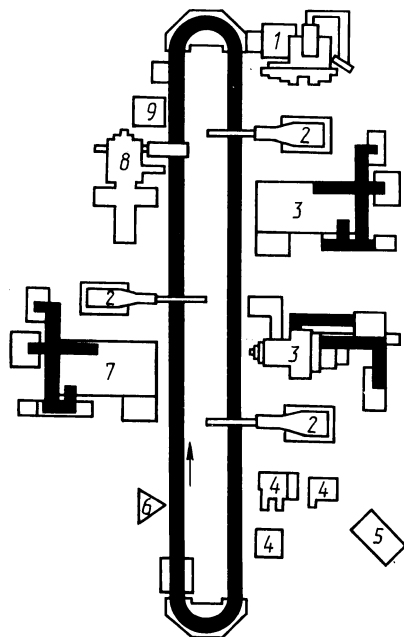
Гибкая технологическая система: 1 — шлифовальный станок; 2 — робот; 3 — токарный станок с ЧПУ; 4 — устройство для измерения обработанной детали; 5 — центральная ЭВМ; 6 — зона загрузки-выгрузки; 7 — расточный станок с ЧПУ; 8 — сварочная машина; 9 — контроль качества сварки
